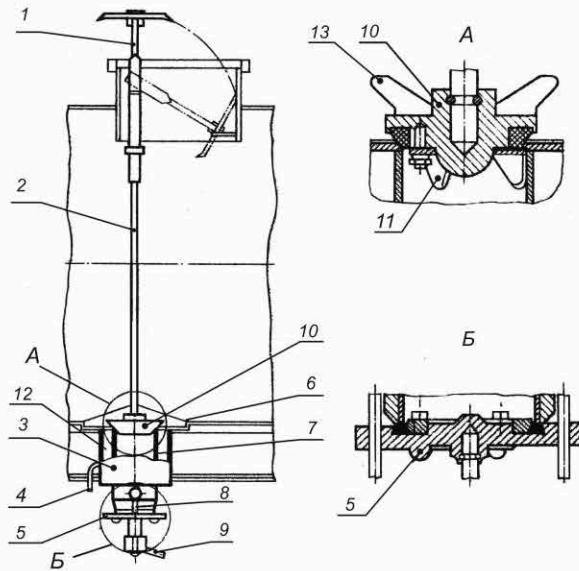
Универсальный сливной прибор с верхним управлением:
